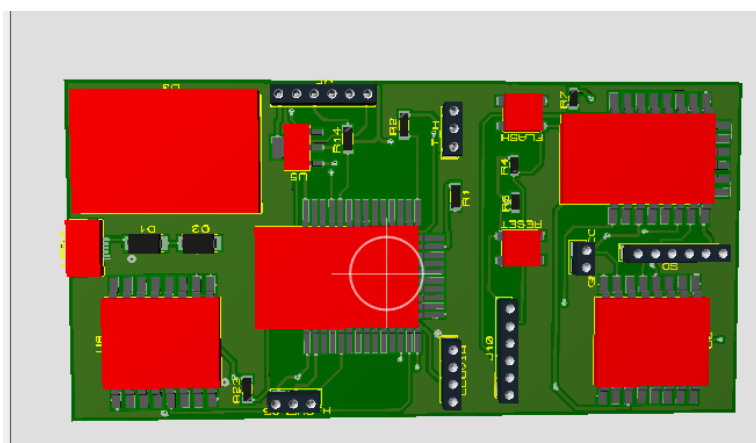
Diseño frontal de la PCB dispositivo Base y Dispositivo Nodo. Fuente: Elaboración propia
